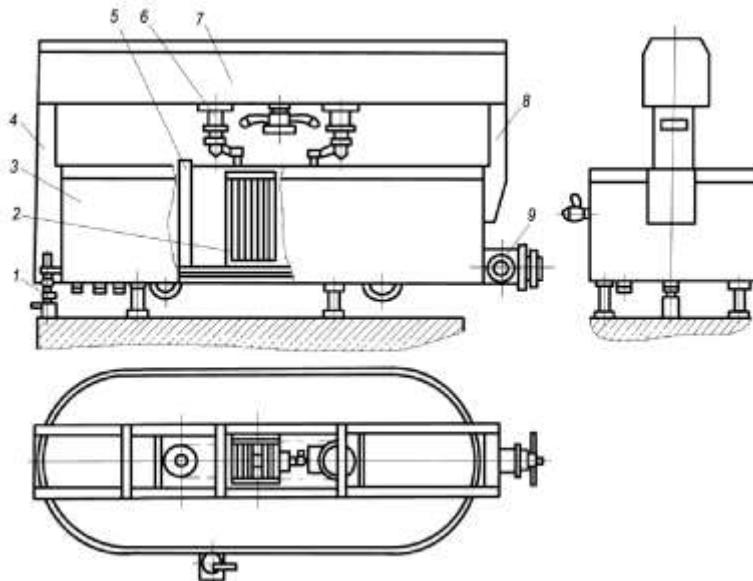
Схема ванни для виготовлення сирного зерна:
